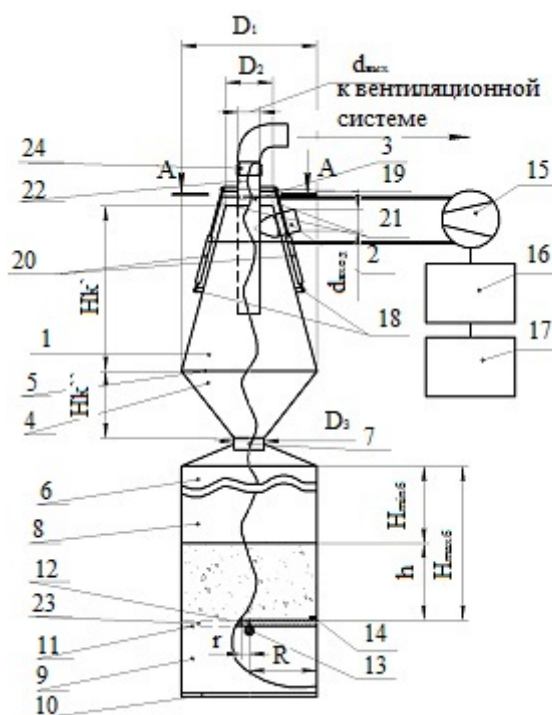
ЦОК: 1 — верхний конус циклона; 2 — входной патрубок; 3 — выхлопной патрубок; 4 — нижний конус циклона; 5 — основания конусов; 6 — пылесборник; 7 — патрубок; 8 — верхний отсек пылесборника; 9 — нижний отсек пылесборника; 10 — задвижка; 11 — перегородка; 12 — полукруглые люки; 13 — противовесы; 14 — ось, относительно которой вращается перегородка; 15 — нагнетательное устройство; 16 — блок управления; 17 — источник питания; 18 — кольцевой упор; 19 — проушины; 20 — основания пневмоцилиндров; 21 — выдвигаемые штоки пневмоцилиндров; 22 — шкала с делениями; 23 — кольцевой упор; 24 — гофра, соединяющая выхлопной патрубок с вентиляционной системой
